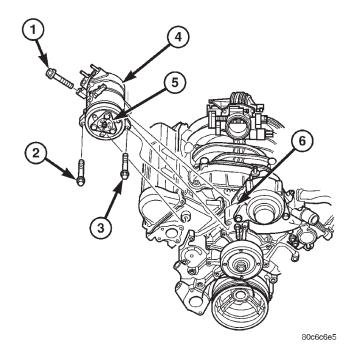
COMPRESOR DE A/A - MOTOR 3.7L
